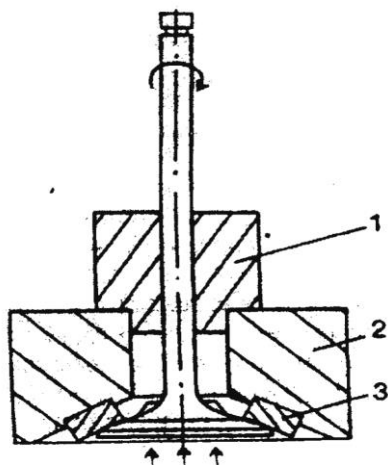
Загальна схема обробки фаски клапана різцевою головкою: 1 – втулка, що центрує; 2 – різцева головка; 3 – твердосплавний різець
